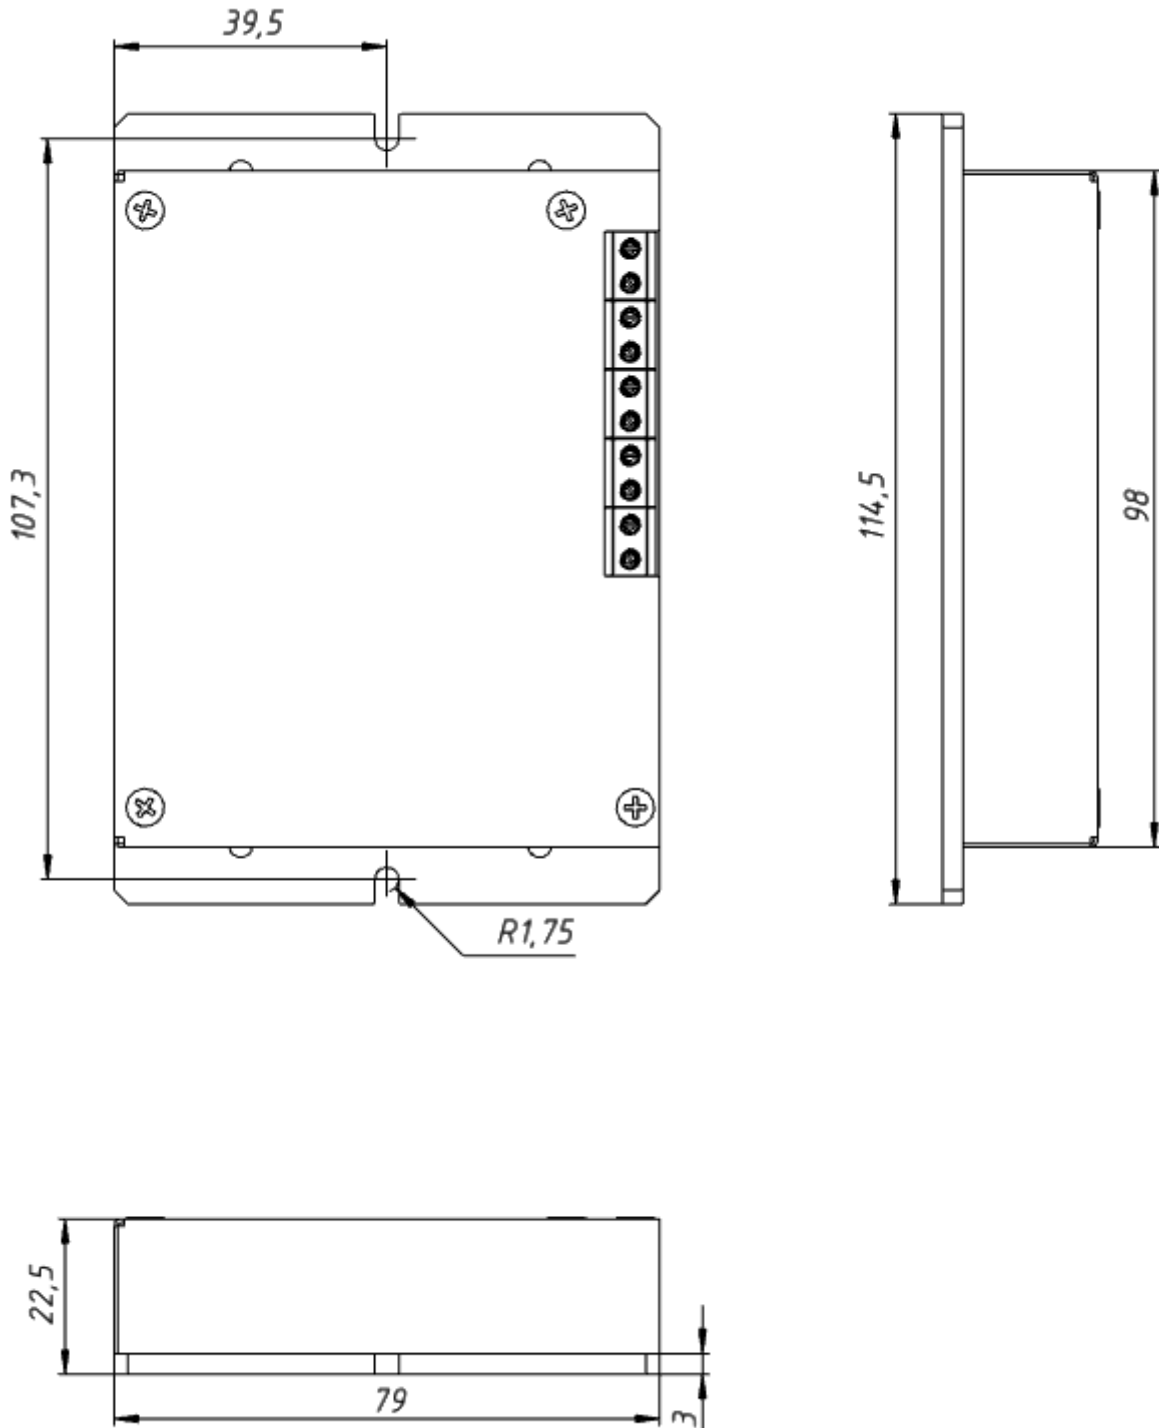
Габаритные и присоединительные размеры устройства
